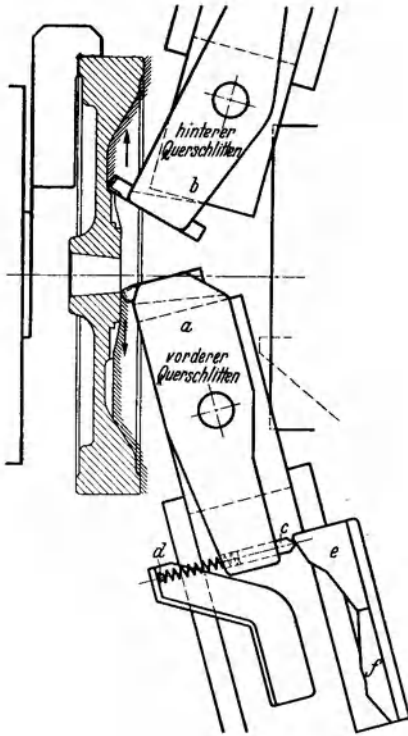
Bearbeitung einer Schwungscheibe. In der Abbildung ist gezeigt, wie es möglich ist, große Planformen von den Querschlitten aus zu drehen. Die Aufgabe wird gelöst durch große schwenkbare Stahlhalter *a* und *b* auf den Oberschlitten der Querschlitten. Diese Stahlhalter tragen am hinteren Ende Taststifte *c* und werden durch Druckfeder nach außen gedrückt. Am Unterteil der Querschlitten sind auf einer besonderen Platte, Kurvenleisten *e* und *f* befestigt, an denen der Taststift beim radialen Vorgehen des Oberschlittens entlang gleitet. Dieselbe Anordnung ist auch auf den hinteren Querschlitten getroffen.
